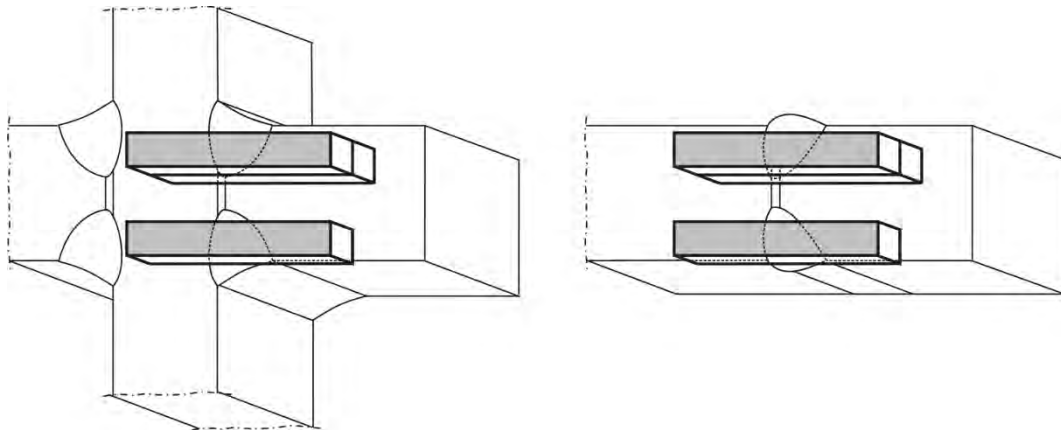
Entnahme der Rohlinge für die Zugproben aus den Schweißanschlüssen
